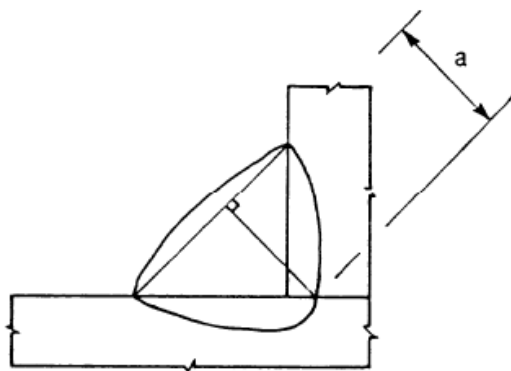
Espessura de um cordão de soldadura com elevada penetração, [4].
